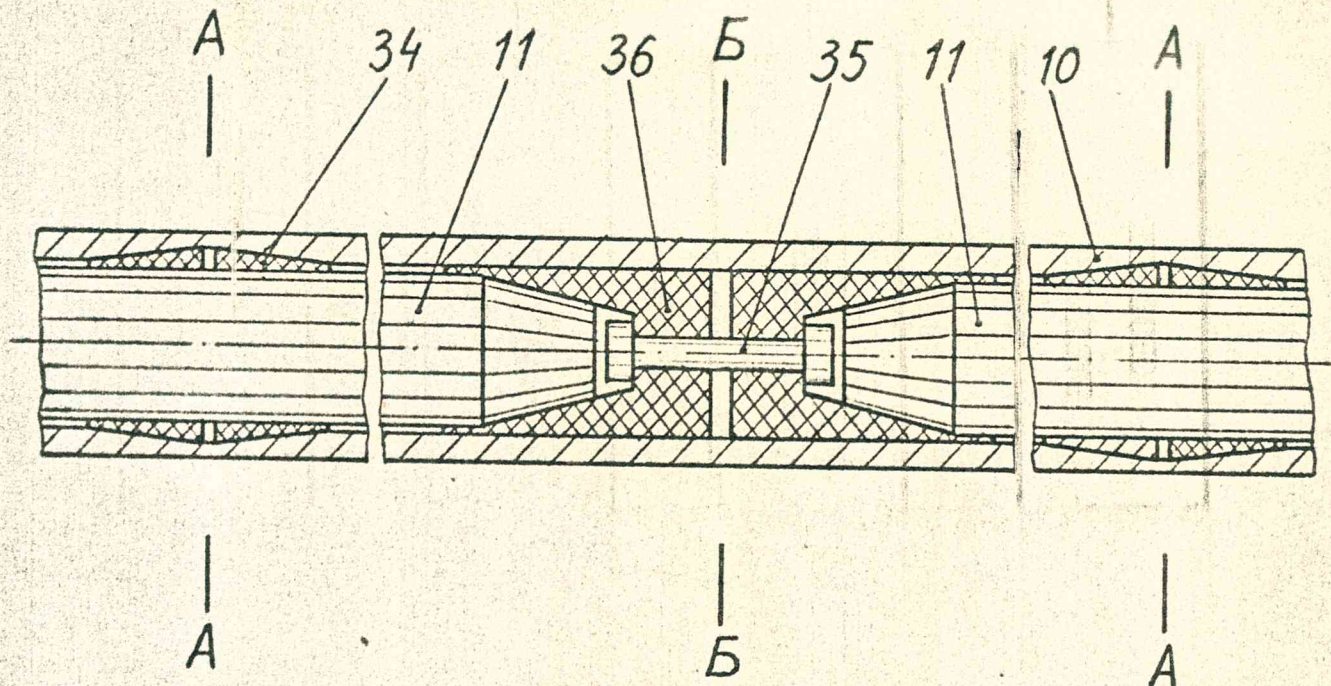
34 - фрикцион корпуса ротора; 35 - разрушаемый стержень; 36 - фрикцион сердечника ротора; А-А - разрушаемое сечение в корпусе ротора; Б-Б - сечение, в котором происходит разделение сердечника ротора.
